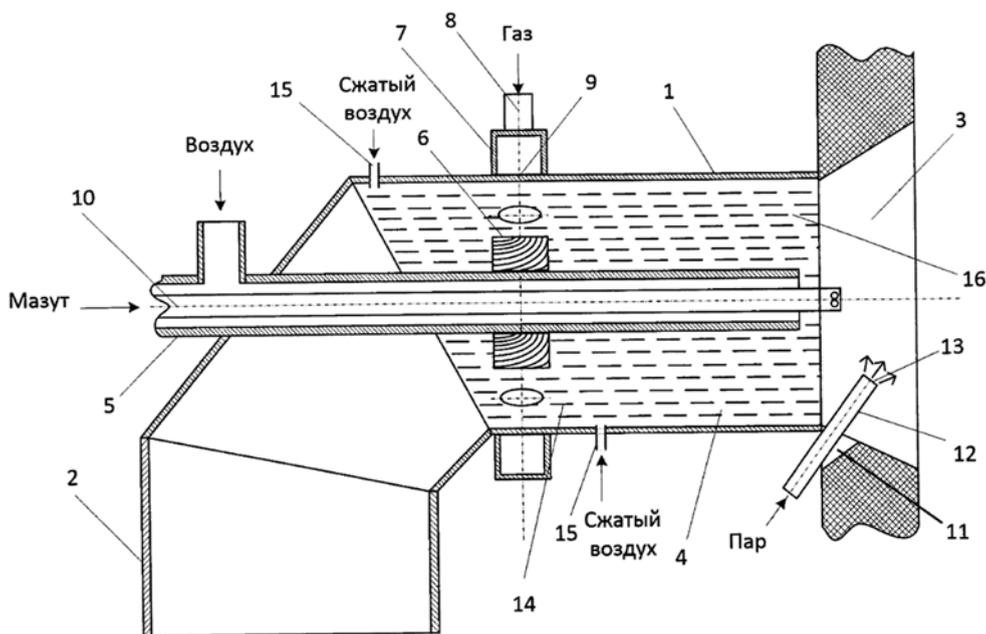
Фронтальный разрез ГУ новой конструкции типа ГП (Патент 208146)
